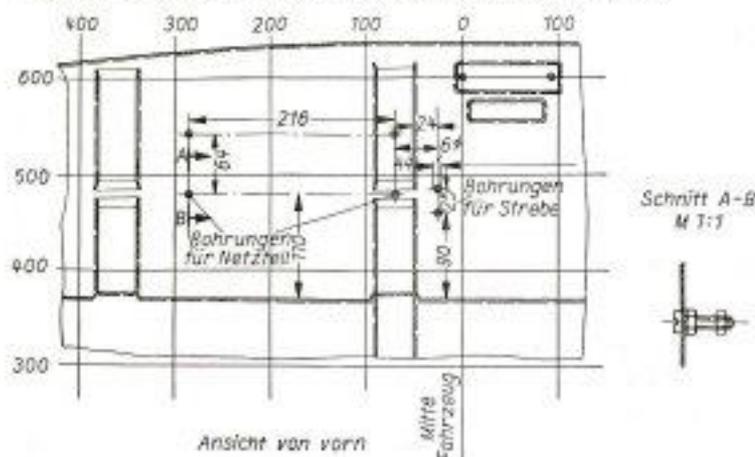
Skizze zum Bohren der Löcher für Befestigung des Netzteiltes und der Strebe
